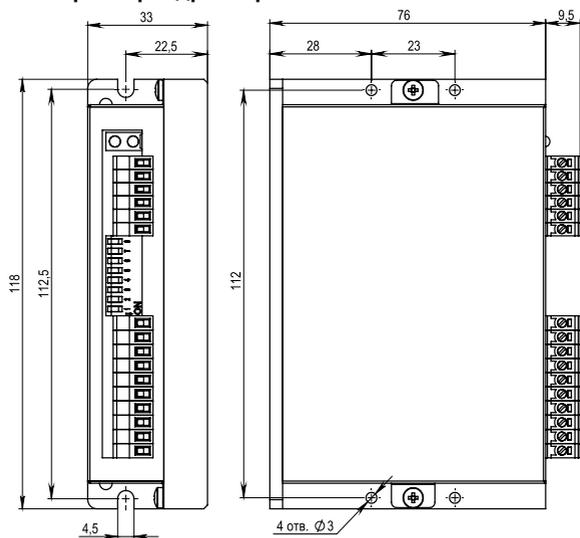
габаритные размеры драйверов SMD-20.24.40.2IR
